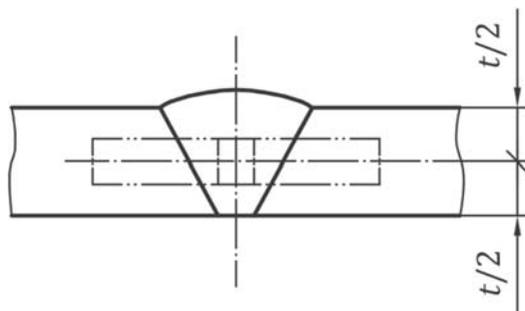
Position de l'éprouvette entaillée d'essai de flexion par choc dans la pièce d'essai
